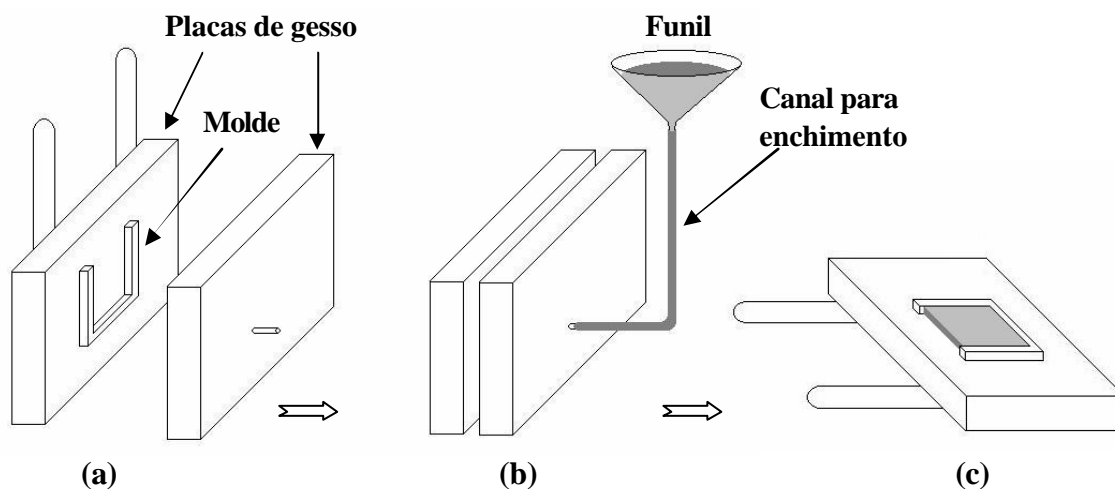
Representação esquemática da estrutura montada para obtenção de placas ( $100 \times 150 \text{ mm}^2$ ) por enchimento por barbotina: (a) colocação do molde entre as placas de gesso; (b) enchimento de barbotina por um canal; e (c) desmoldagem.
